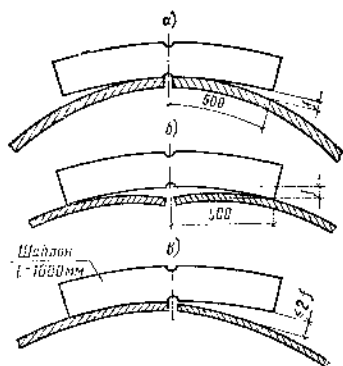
Схема проверки геометрической формы шаровой оболочки шаблоном (а—в)
